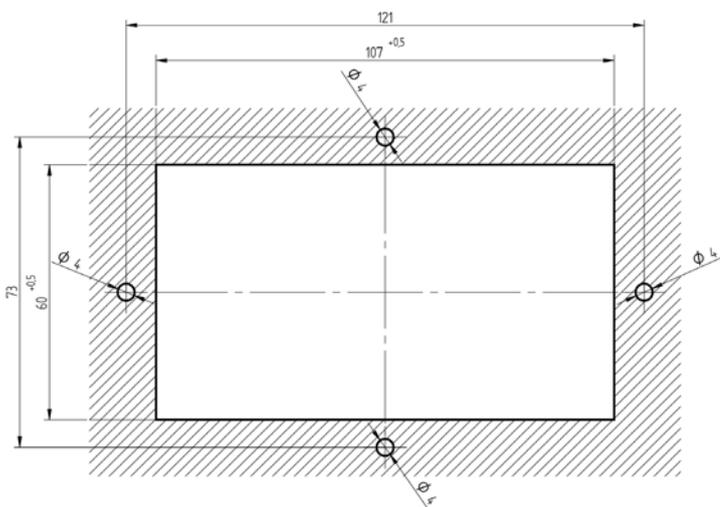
Plan coté de la découpe panneau pour couverture IP65 avec trou de montage
